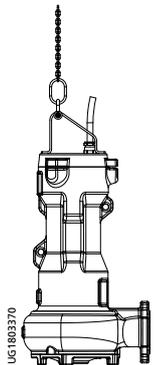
Halterung montieren bei Seilführung, 1-Stangenführung und Bügelführung
